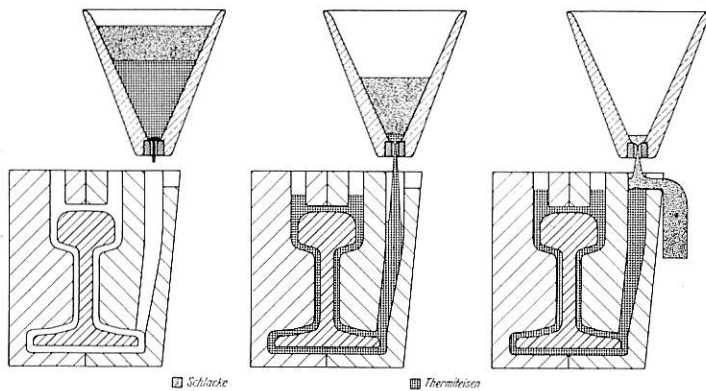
Bildliche Darstellung einer Zwischengußschweißung.
